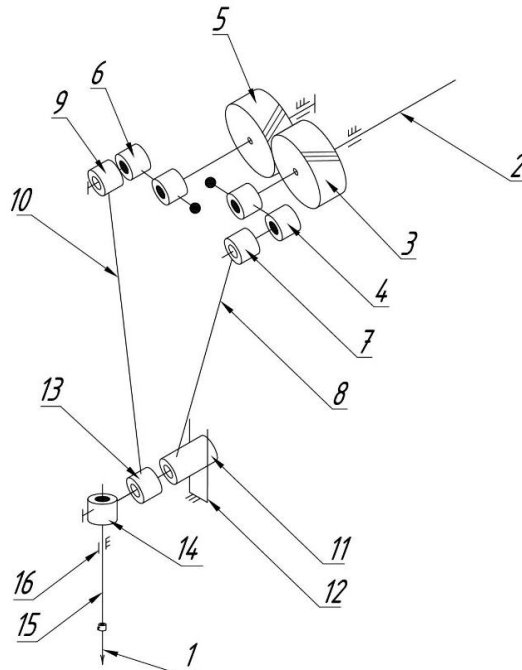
Кінематична схема механізму голки швейної машини розгалуженої конструкції
